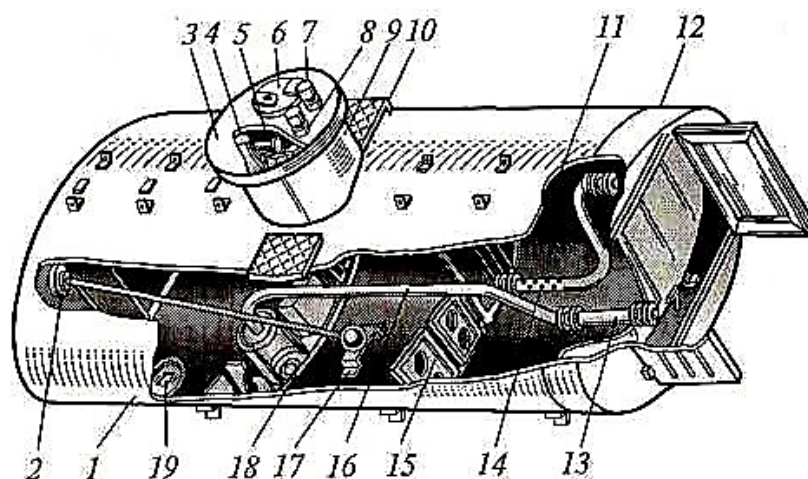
Цистерна для перевозки нефтепродуктов: 1 – цистерна; 2 – патрубок; 3, 6 – крышки; 4 – угольник; 5 – кронштейн; 7 – клапан; 8 – поплавок; 9 – горловина; 10 – подножка; 11 – трубка; 12 – шкаф; 13, 14, 16 – трубопроводы; 15 – волнорез; 17, 19 – опоры; 18 – указатель уровня нефтепродукта
